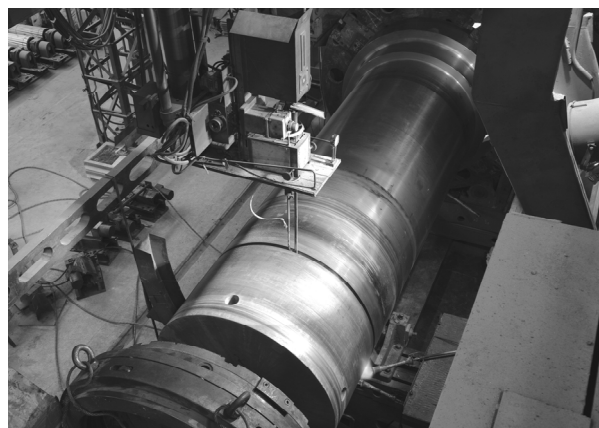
Автоматическая дуговая сварка в узкую разделку цилиндра прессы 70 МН (заказчик НВЕ, Корея 2008 г.)
